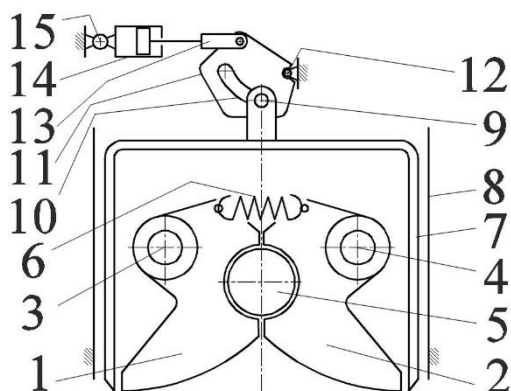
Схема запорного механізму сидельно-зчіпного пристрою.
